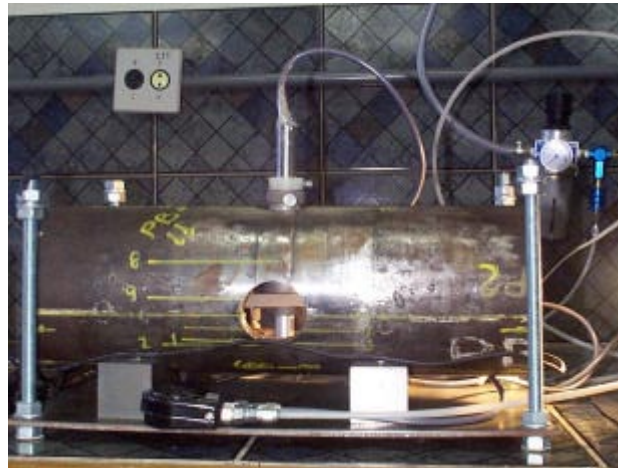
Montagem do ensaio para medição interna: o Drill Hole posicionado dentro do tubo.
